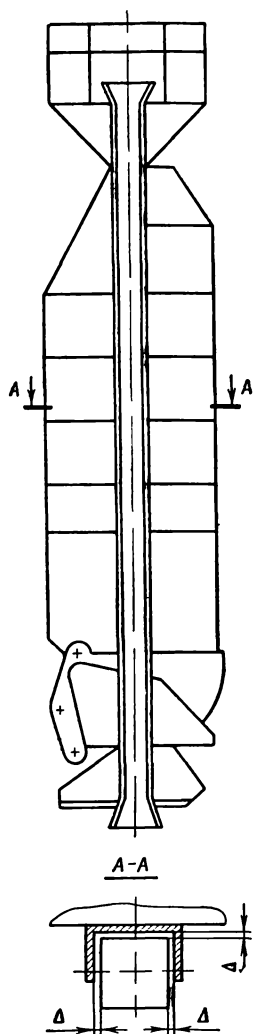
Схема конструкции скипа с непрерывными корытообразными направляющими для деревянных проводников
